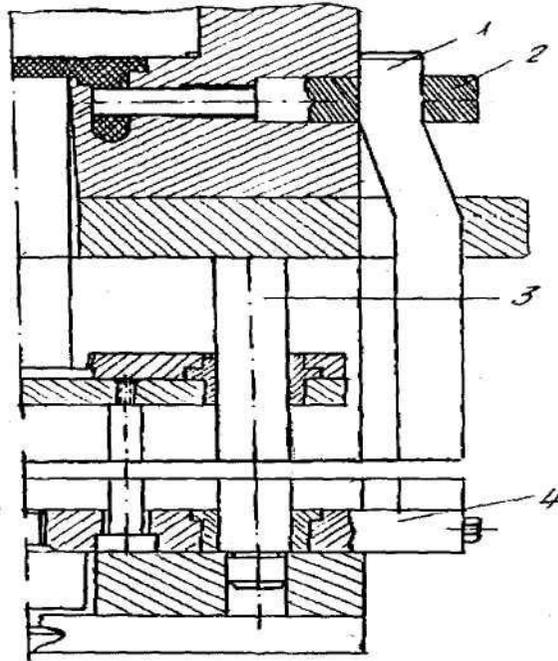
Схема устройства шибера, работающего от выталкивающей системы пресса:
